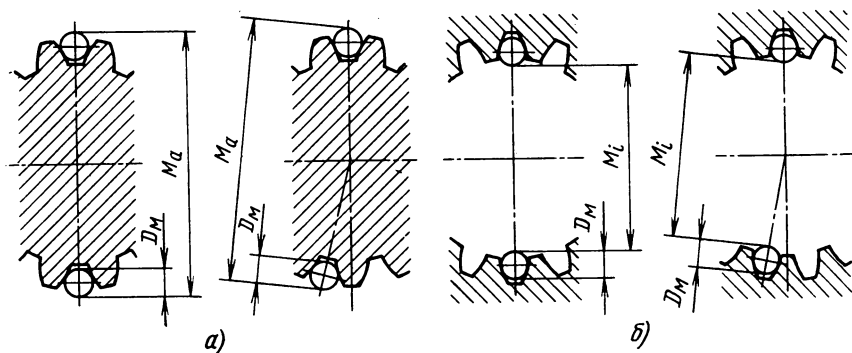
Схема контроля толщины зубьев вала (а) и ширины впадин втулки (б) эвольвентного шлицевого соединения
